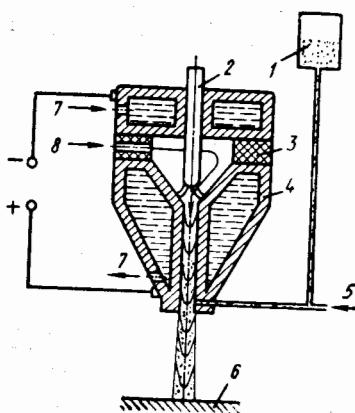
Схема плазмотрона для напыления металлического порошка:
